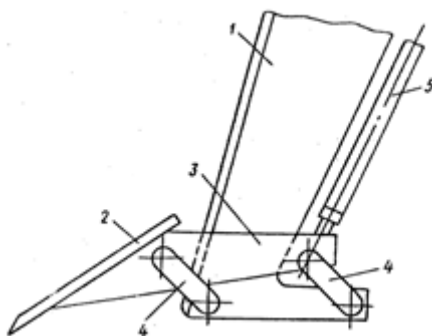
Рабочий шарнирно – соединенный орган рыхлителя
